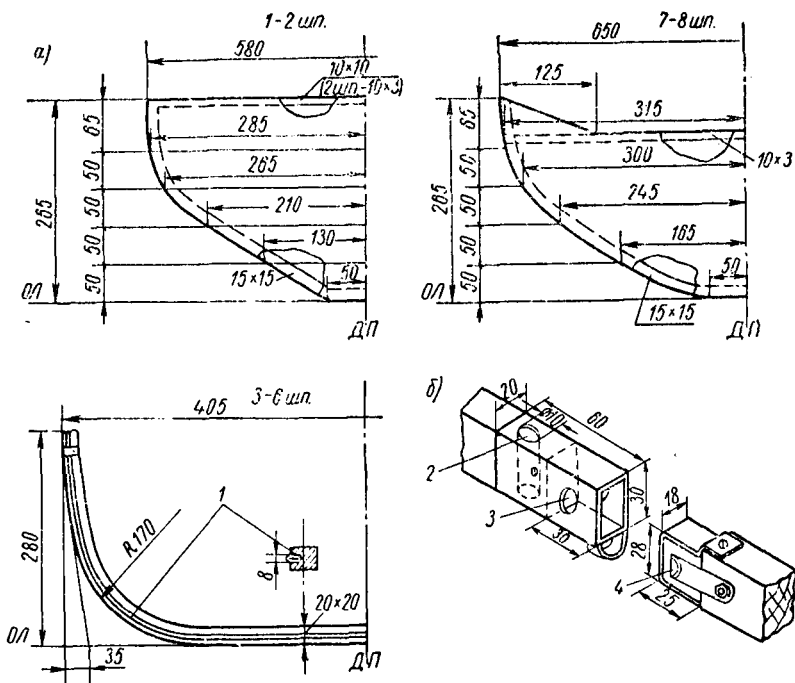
«Ладоба» M2-Б: а — шпангоуты (1, 3, 5 и 7 шп. — см. в нос; 2, 4, и 8 шп. — см. в корму; 4 и 6 шп. — без паза для уплотнителя); б — шиповое соединение привального бруса.
